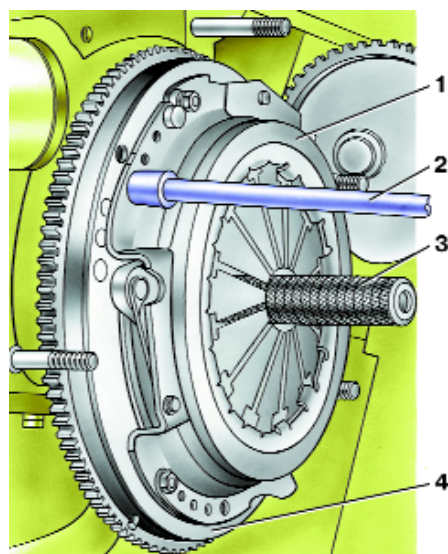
Установка сцепления в сборе на маховик двигателя: 1 – нажимной диск сцепления с кожухом в сборе; 2 – торцовый ключ; 3 – оправка; 4 – маховик
